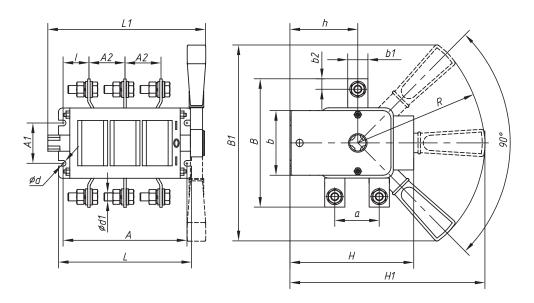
Выключатель-разъединитель универсальный трехполюсный на два направления с д/г камерами, несъемная левая/правая рукоятка
